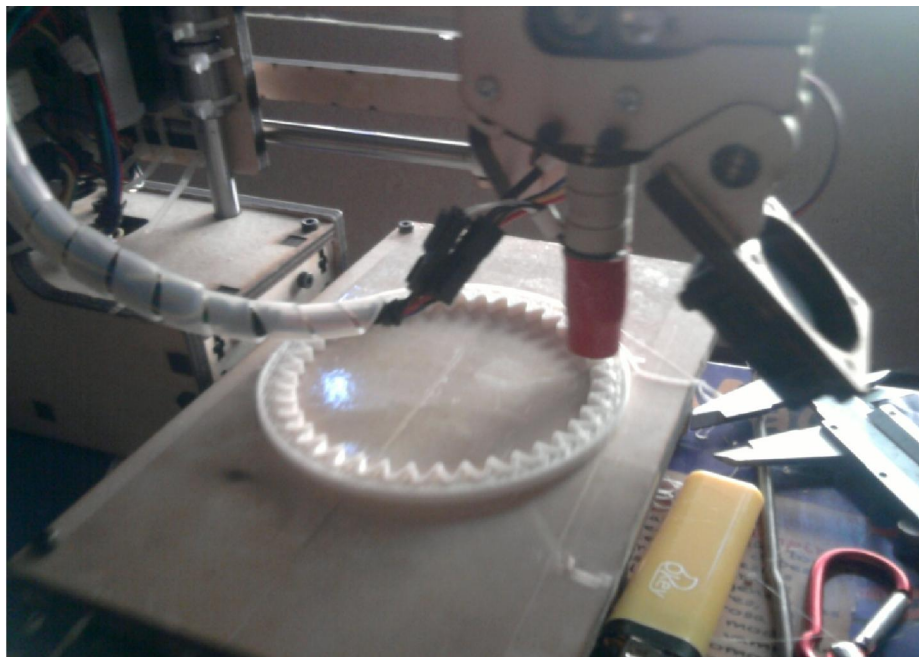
Impresión de engranaje interior en PLA $m=1.5$
